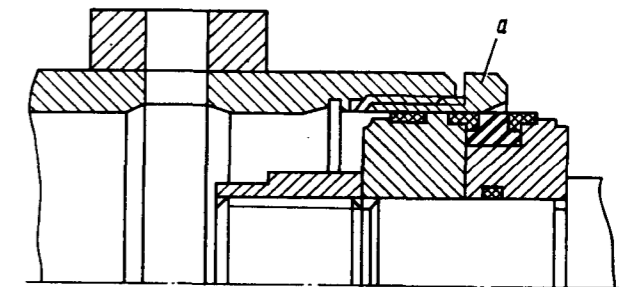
Приспособление для монтажа поршня в гидроцилиндр II типа:
